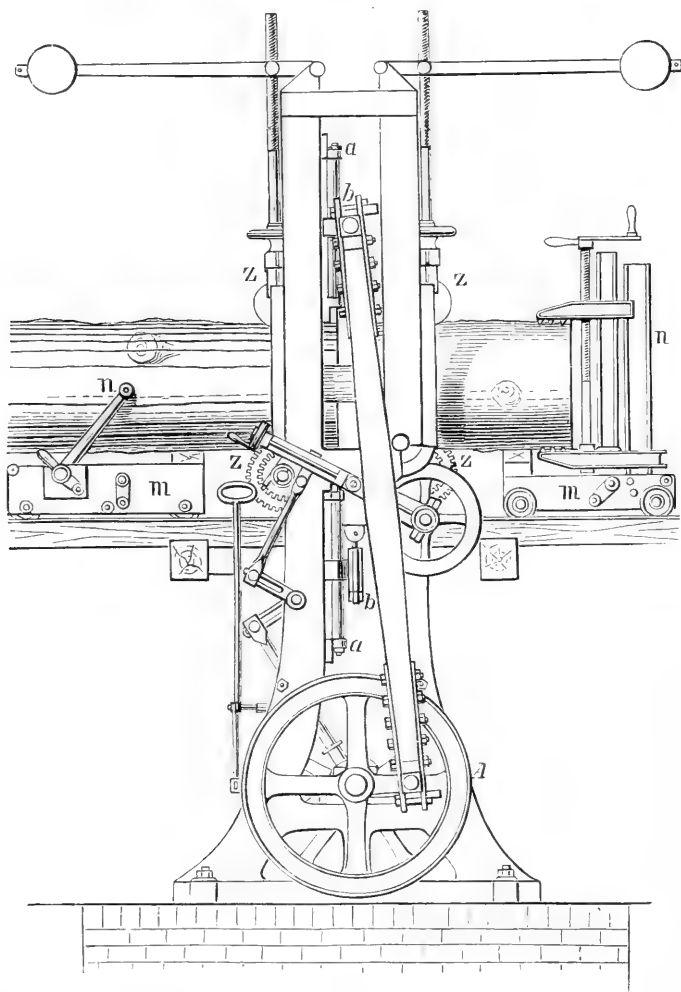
Konstruktion einer Dampfäge mit Vollgatter.
